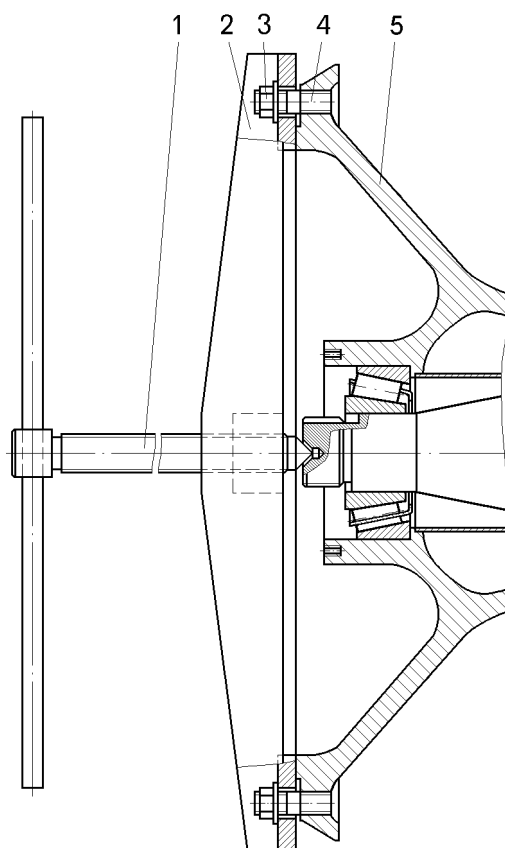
Приспособление для съема ступиц передних колес:
